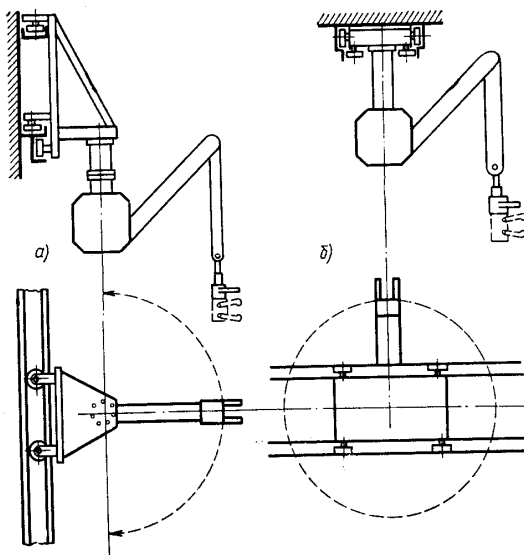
Схема шарнирно-балансирного манипулятора
